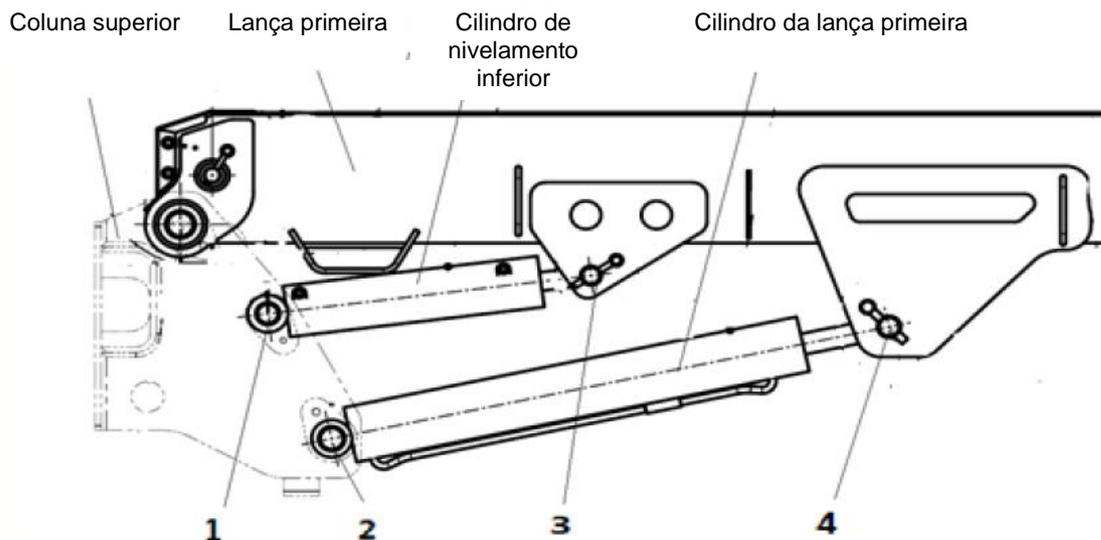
Diagrama de desmontagem do cilindro de levantamento inferior e cilindro de levantamento da lança superior
